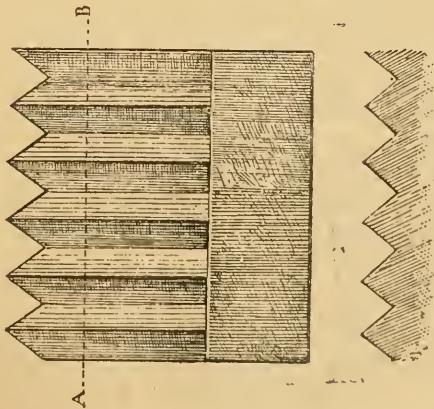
et 31. — Couteau du coupe-pommes en plan et en coupe suivant A B.
